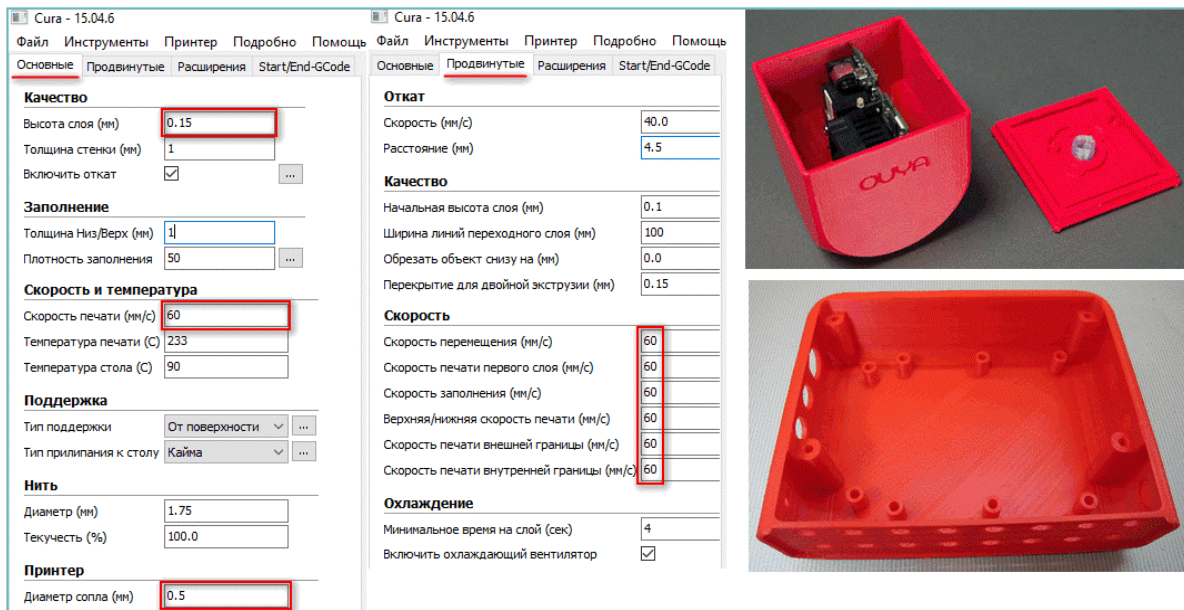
Параметры печати для корпусов приборов и пластинчатых деталей [26]
